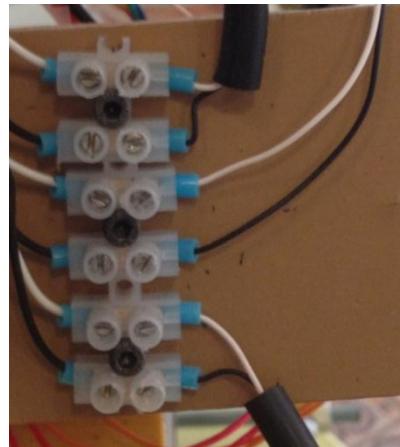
Montaje de los finales de carrera (paso 5). Colocación de los cables en las clemas
